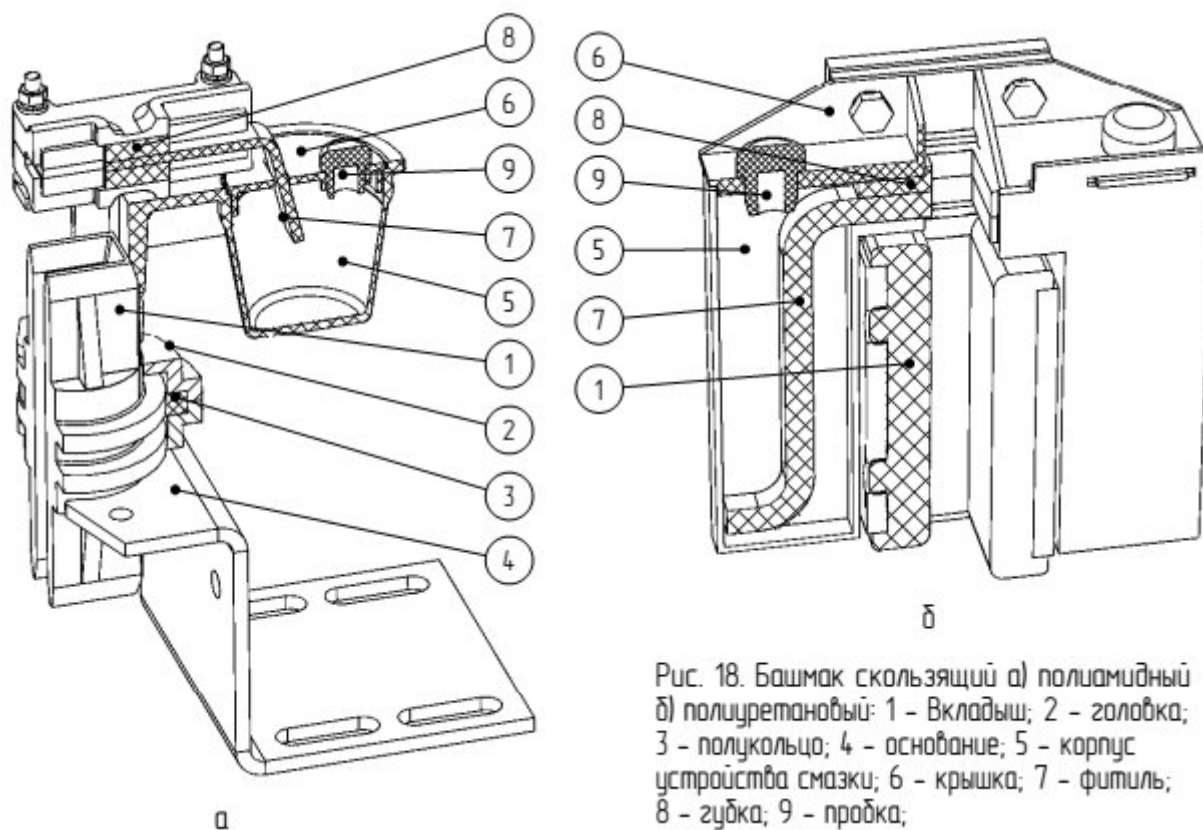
Башмак скользящий а) полиамидный б) полиуретановый: 1 - Вкладыш; 2 - головка; 3 - полукольцо; 4 - основание; 5 - корпус устройства смазки; 6 - крышка; 7 - фитиль; 8 - губка; 9 - пробка;
